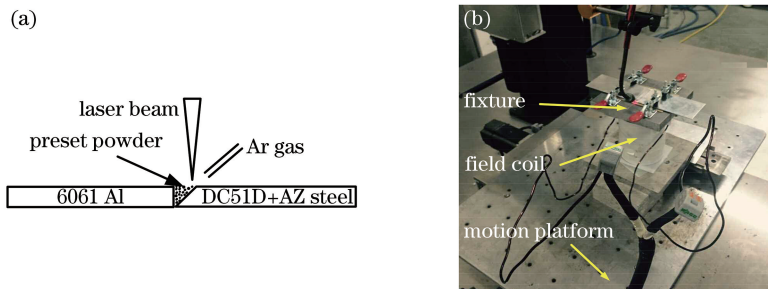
激光焊接试验(a)示意图和(b)装置
